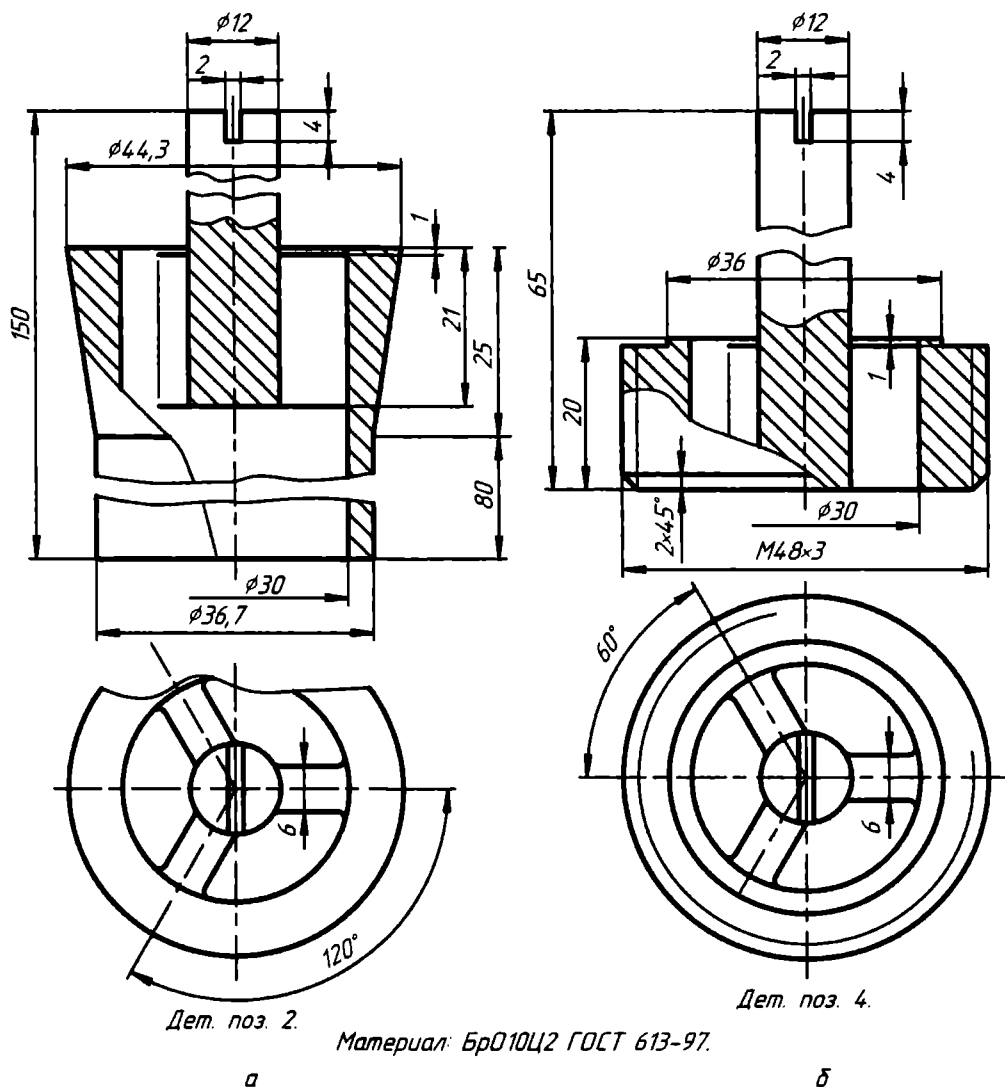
Чертежи седла клапана: а — всасывающего; б — нагнетательного
